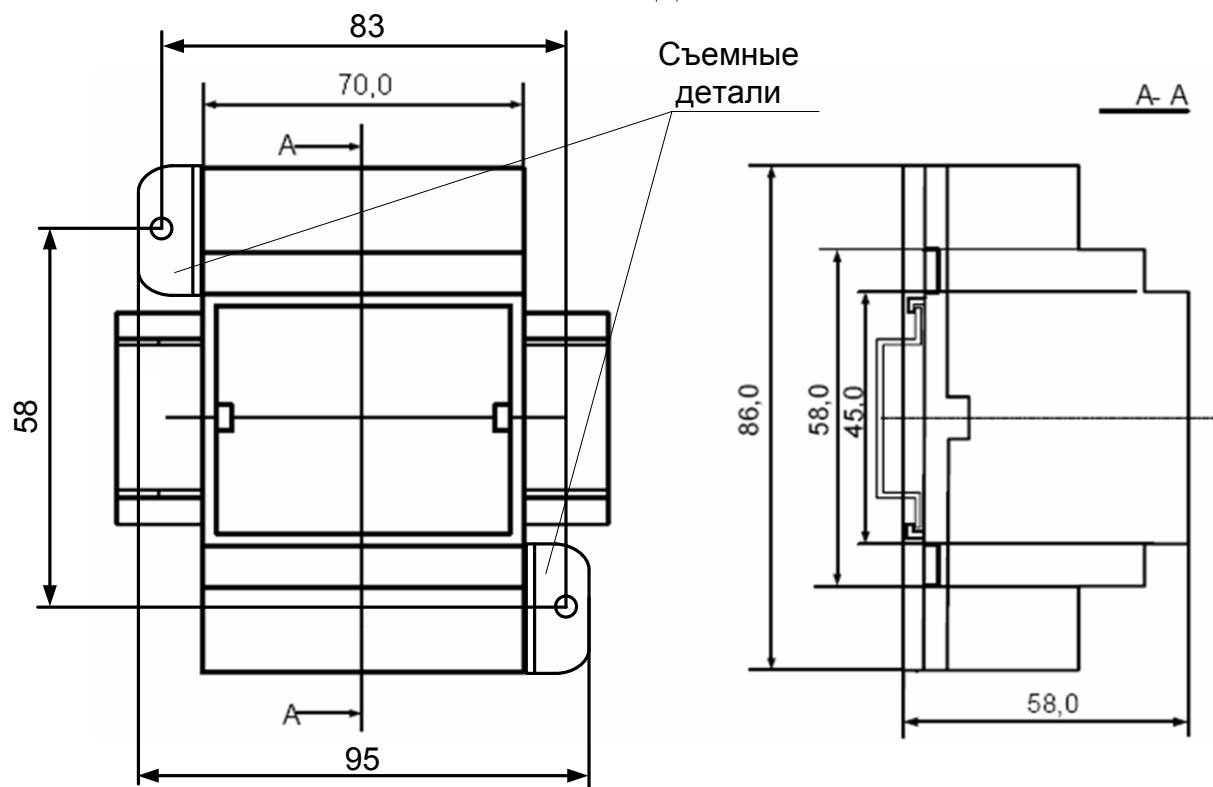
Габаритные и присоединительные размеры блока питания PSM-36-24
